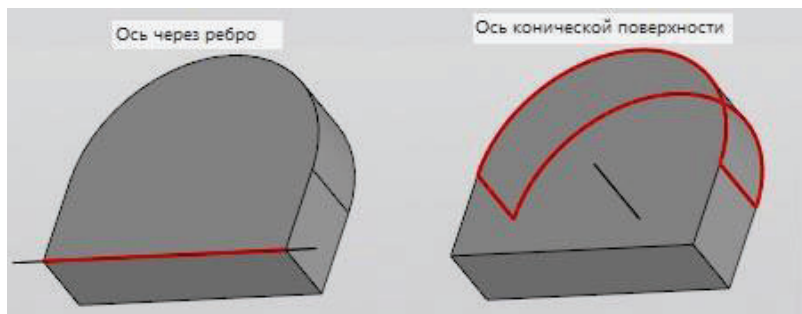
Ось конической резьбы / Ось через ребро
